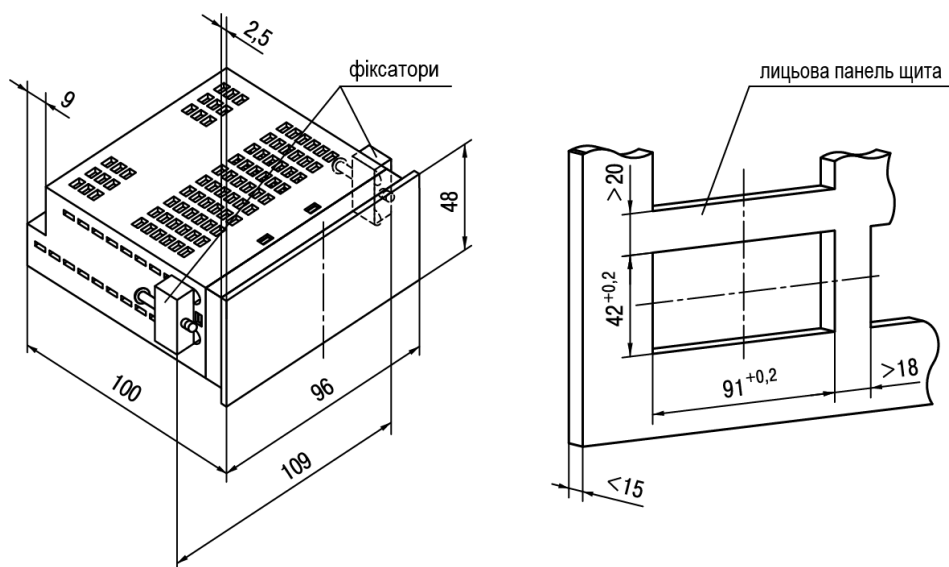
Габаритні розміри корпусу Щ2
